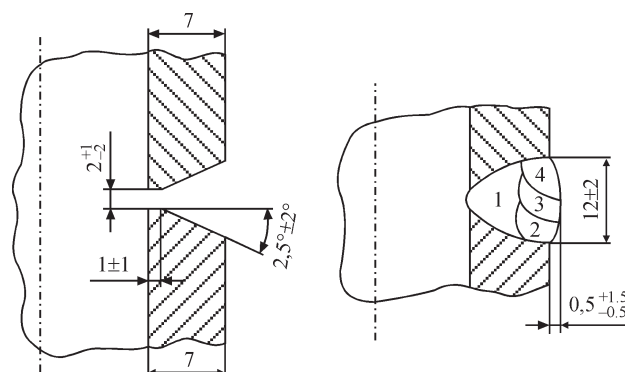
Підготовка кромки одного U-типу для зварних з'єднань труб (процес зварювання SMAW) (а), передбачувана конфігурація зварного шва та розташування зварних валиків (б)
